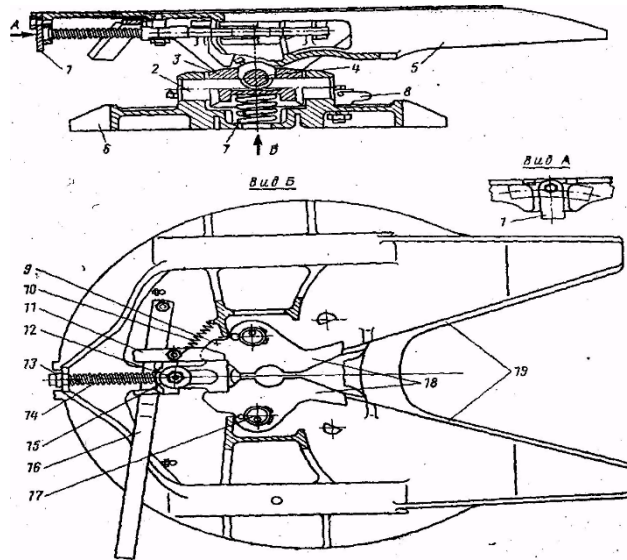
Напівавтоматичний опорно-зчіпний пристрій сидельних автомобілів-тягачів: 1-планка; 2 — поздовжня вісь; 3-балансир; 4-поперечна вісь; 5 - опорне коло; 6-плита; 7-амортизаційні пружини; 8— обмежники бічної хитаючи; 9 — штифт; 10 — пружина; 11 — засувка; 12 — напрямний палець; 13 — стрижень кулака; 14 — пружина; 15 — замок; 16 — важіль замка; 17 — пальці захватів; 18 — захвати; 19 — устя
